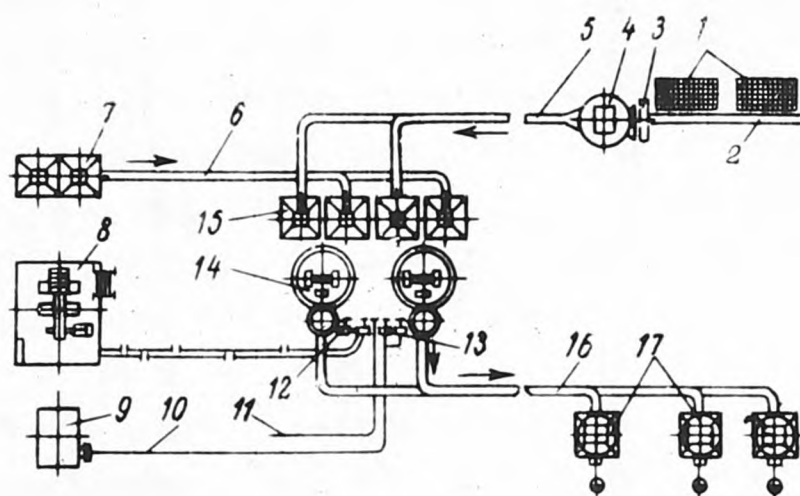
Схема приготовления и транспортирования формовочной смеси в поточном производстве:
